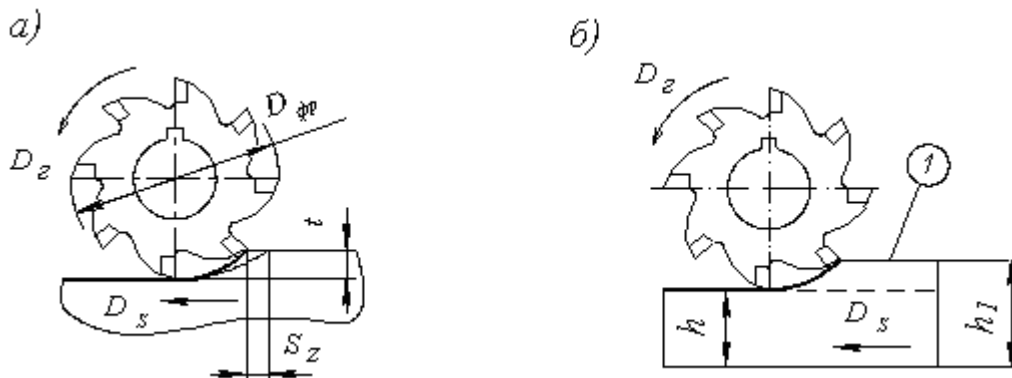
Схема фрезерования (*а*) и схема размерной наладки фрезы (*б*)
